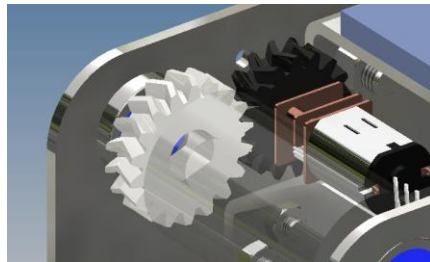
Sistema de transmisión por engranajes tipo Herring-bone
